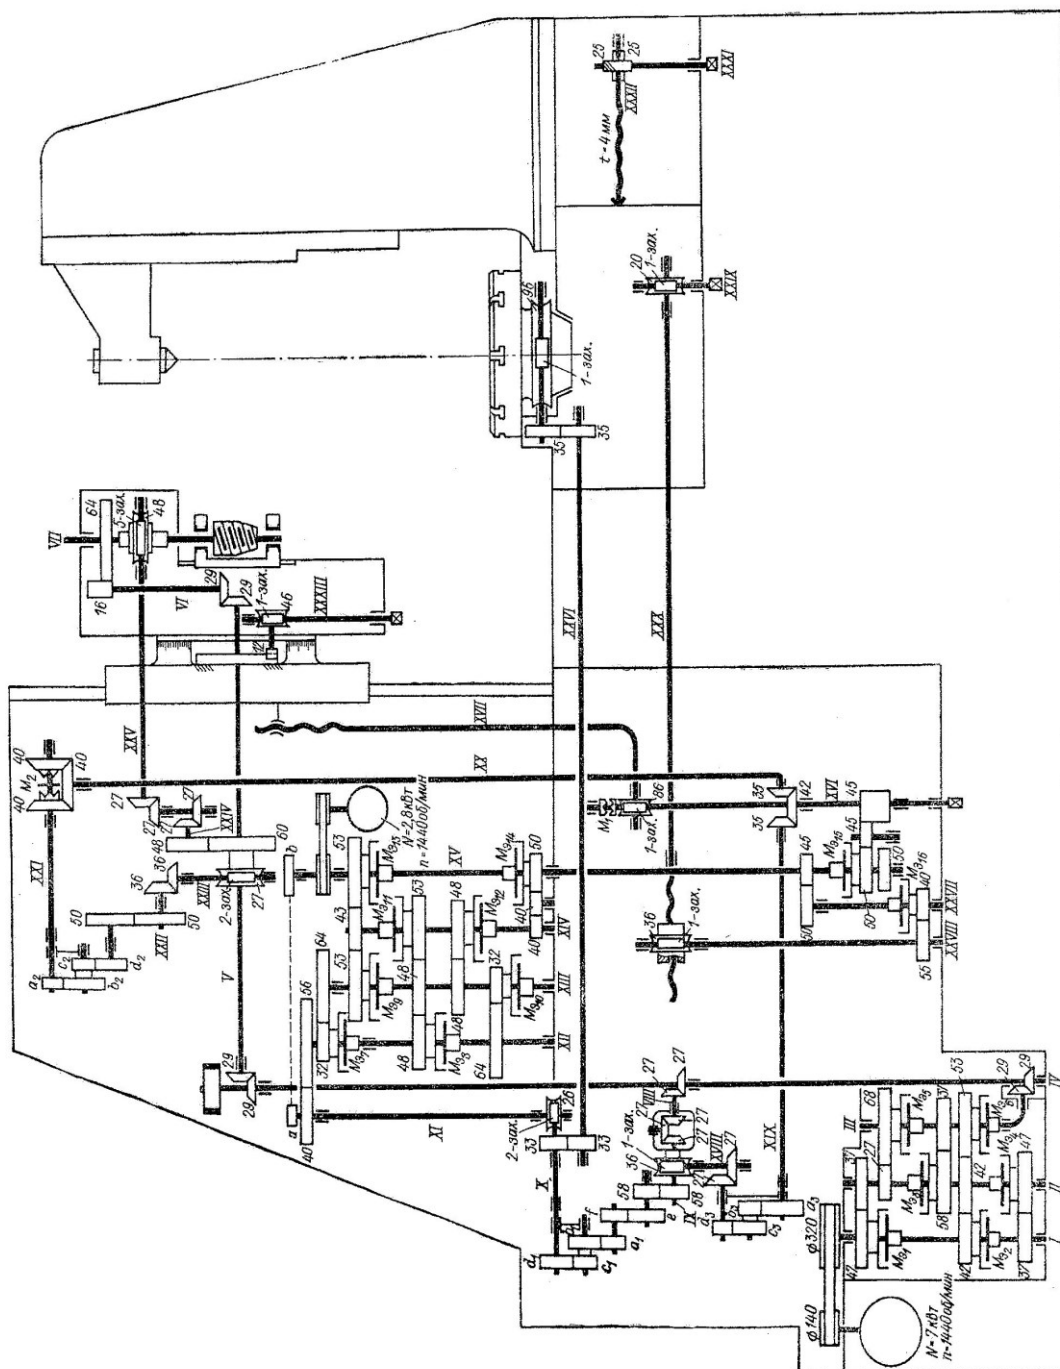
Вертикальный зубофрезерный станок мод. 5К324
